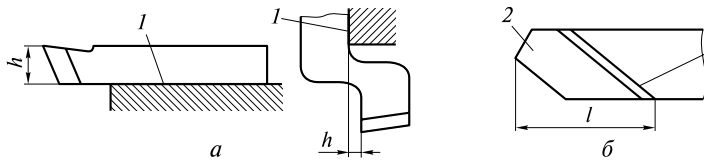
Положение режущей части резца относительно опорной поверхности (а) и поверхность заточки токарного резца (б):
